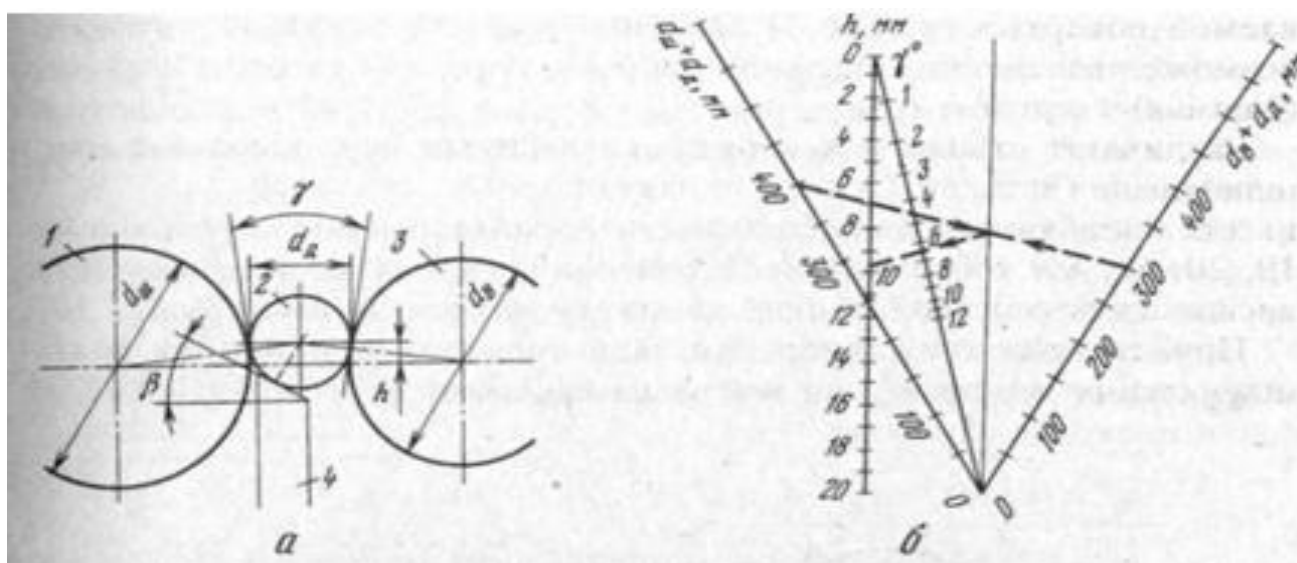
Схема бесцентрового шлифования (а): 1 – шлифовальный круг, 2 – заготовка, 3 – ведущий круг, 4 – опорный нож, d_v – диаметр ведущего круга, d_d – диаметр детали, h – превышение оси заготовки осей кругов, γ – тангенциальный угол, β – угол опоры; номограмма для определения положения детали по высоте (б).
